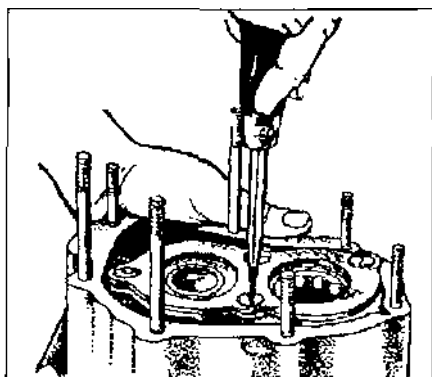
Отворачивание винтов крышки подшипников.
